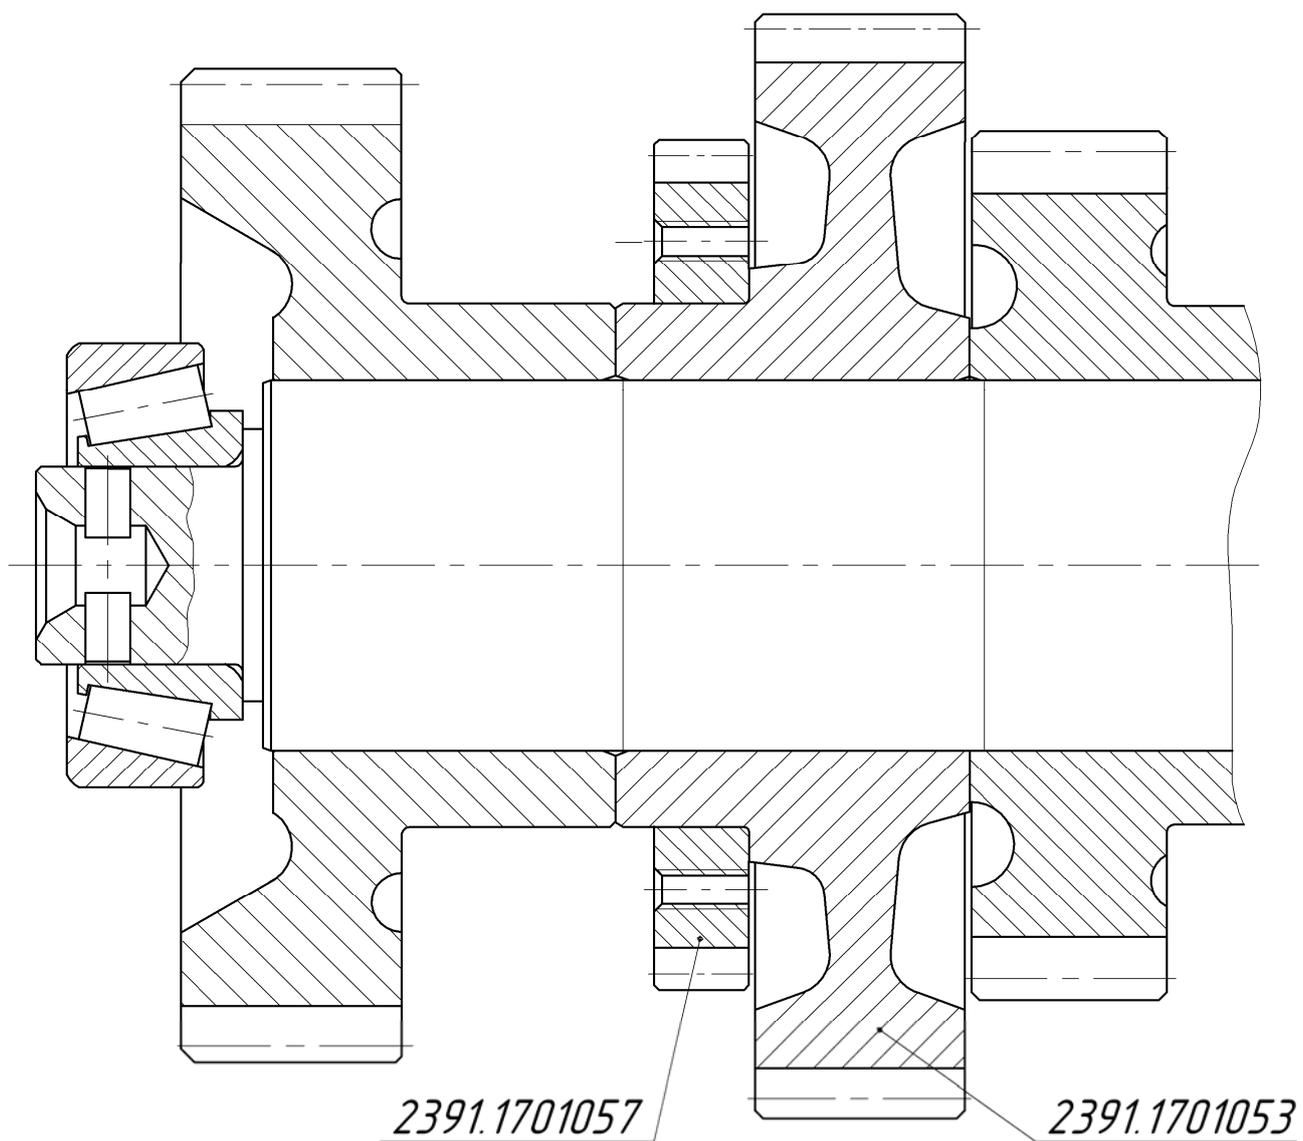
Вал промежуточный в сборе, дет. 239.1701047, КП ЯМЗ-239
